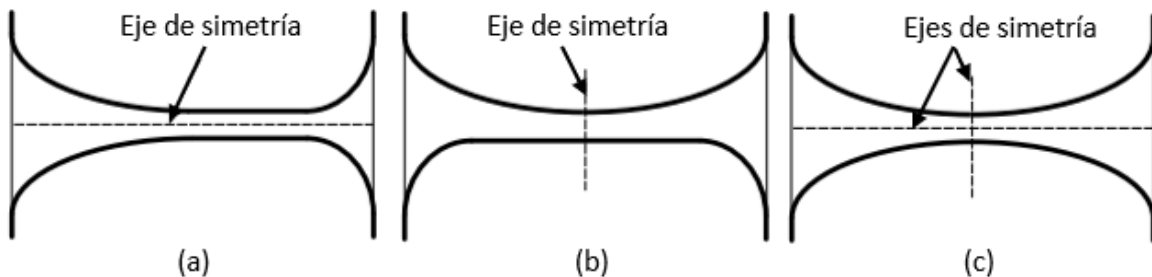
Bisagra flexible con simetría en eje a) longitudinal, b) transversal y c) longitudinal y transversal. Adaptada de Lobontiu (2002).
